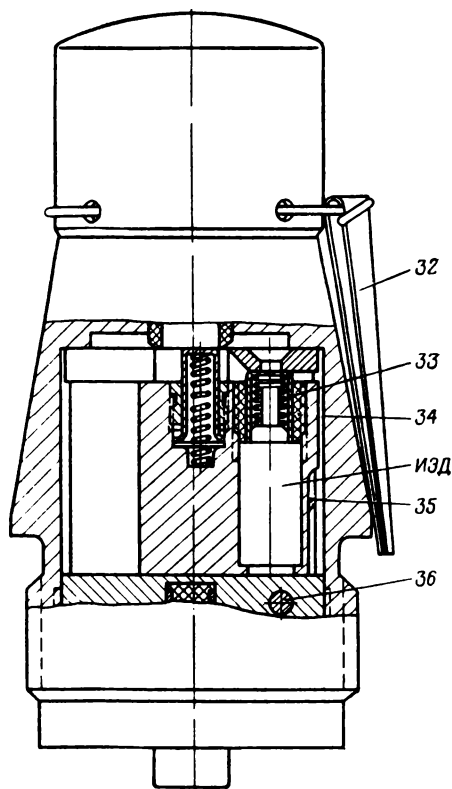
Взрыватель ГПВ-1 (положение деталей до выстрела):
